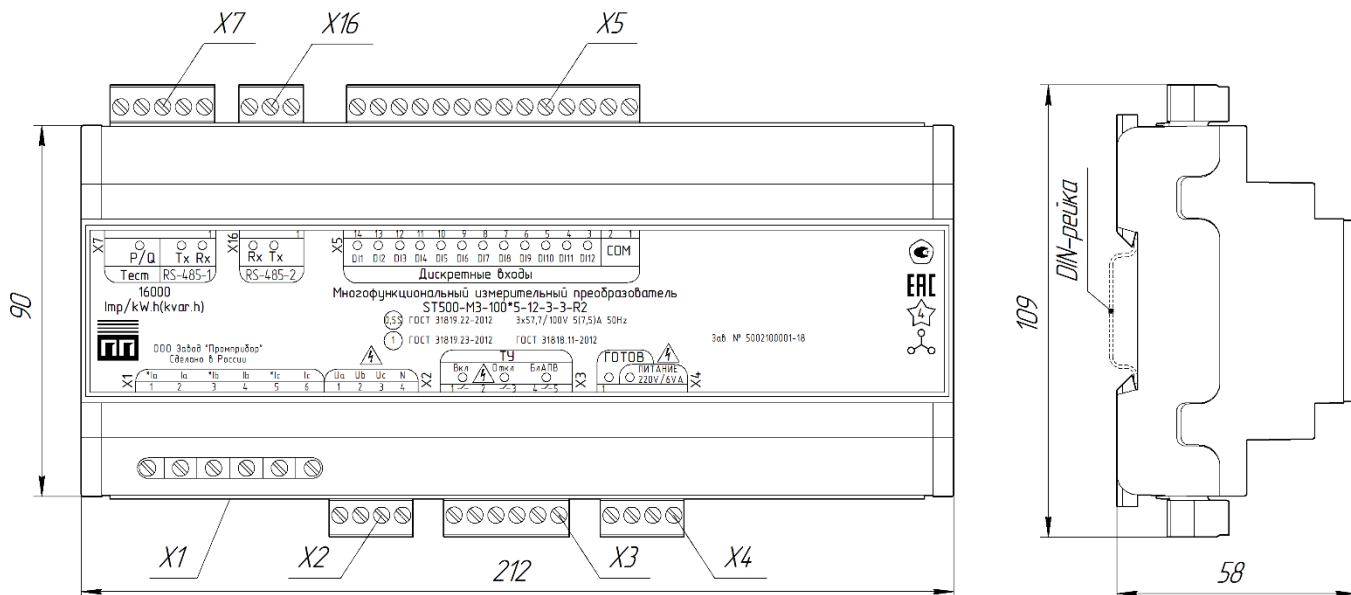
Внешний вид и габаритные размеры МИП
